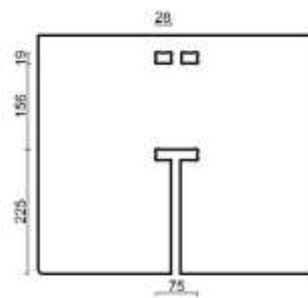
Desenho técnico peça "A" (Fonte: o autor)
